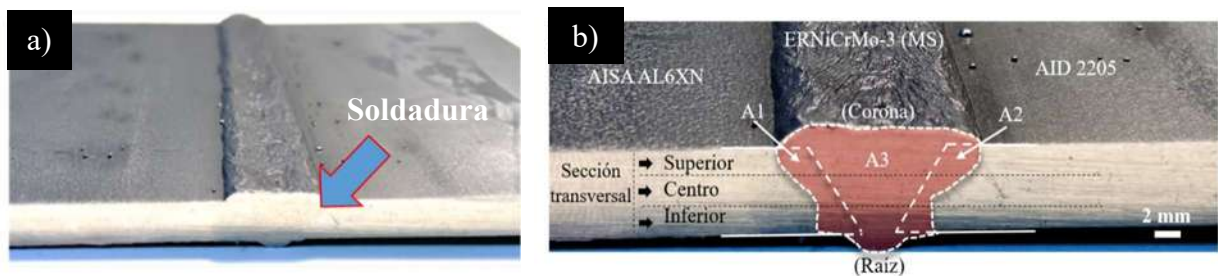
a) junta soldada disímil, y b) sección transversal de la junta soldada.
